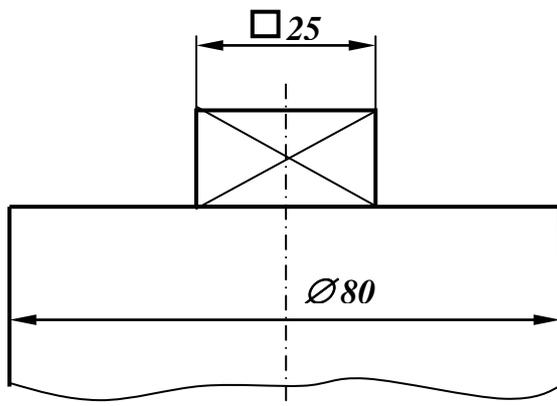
Нанесения размера элемента изделия квадратного сечения
